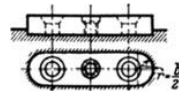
Gewinde in der Mitte für Abdrückschraube.
